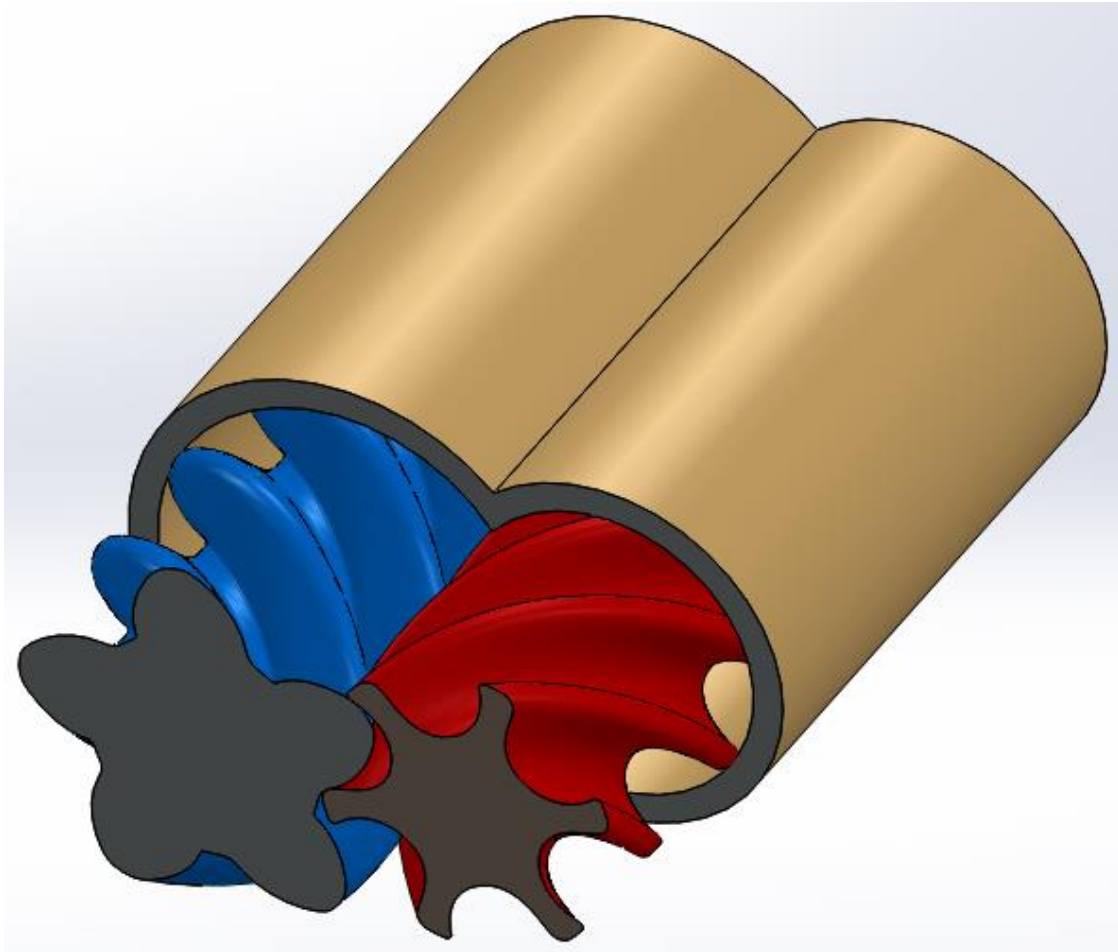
Rotore maschio e rotore femmina accoppiati ed inseriti nell'housing del compressore.
